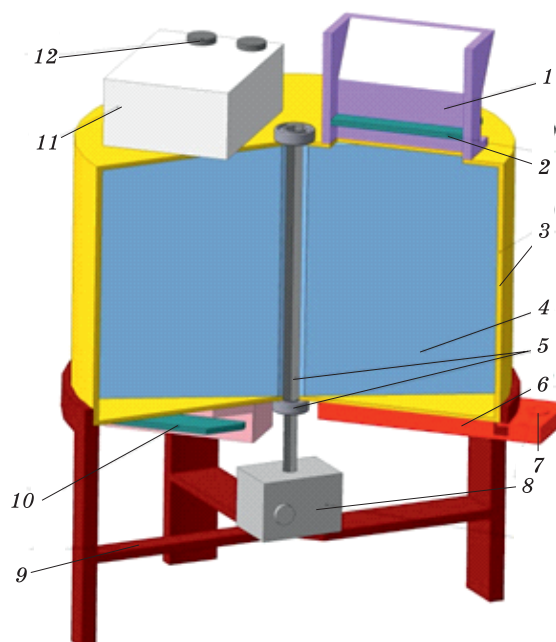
Пространственное изображение СВЧ-индукционной установки барабанного типа для микронизации зерна: 1 – загрузочный патрубок; 2 – заслонка; 3 – цилиндрический корпус; 4 – секционный барабан; 5 – вал барабана; 6 – индукционная плита; 7, 12 – регуляторы мощности; 8 – мотор-редуктор; 9 – монтажный стол; 10 – выгрузной патрубок; 11 – СВЧ-генератор
